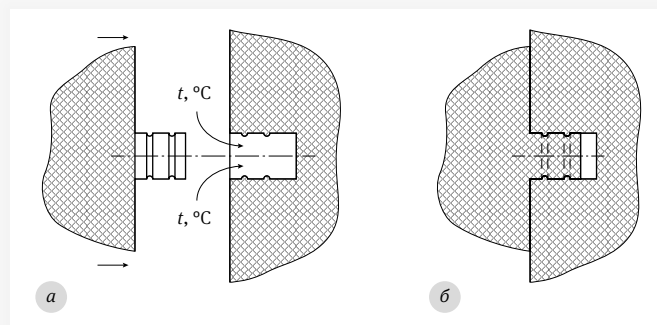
Усовершенствованная сборка модельного блока: а – подготовка к сборке; б – результат сборки
